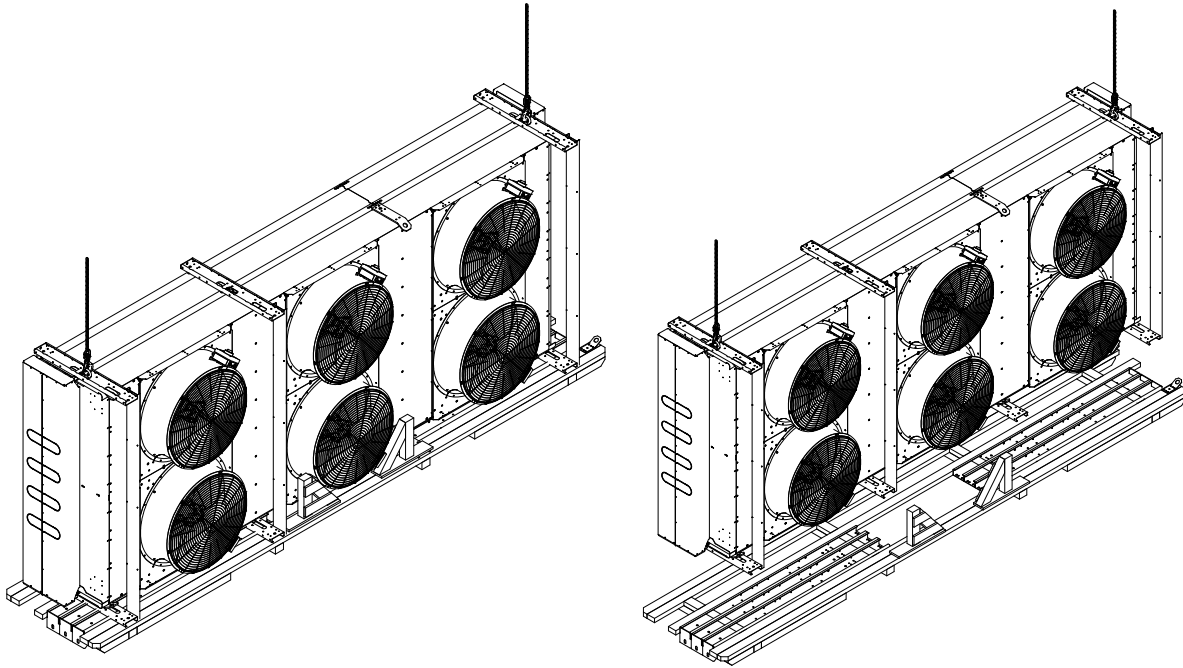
Disposición para el embalaje de las patas de montaje elevado para el transporte en camiones y contenedores
